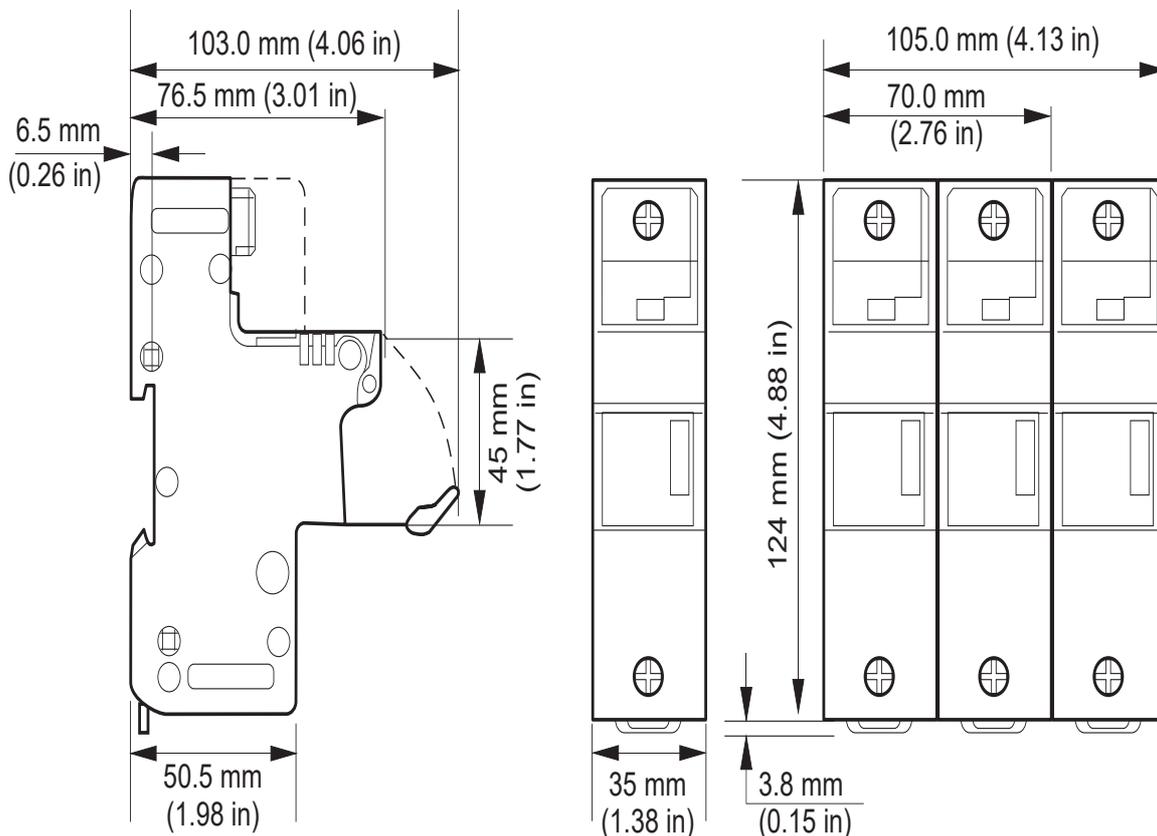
Dimensions du porte-fusible : US221 (22x58 mm)
